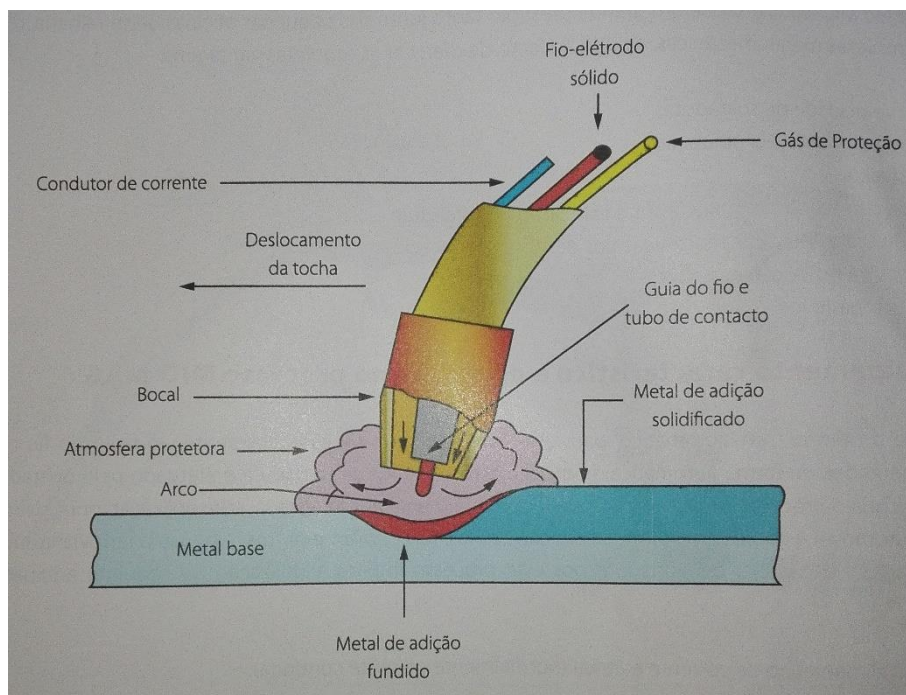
Esquema de soldadura MIG-MAG [17]
